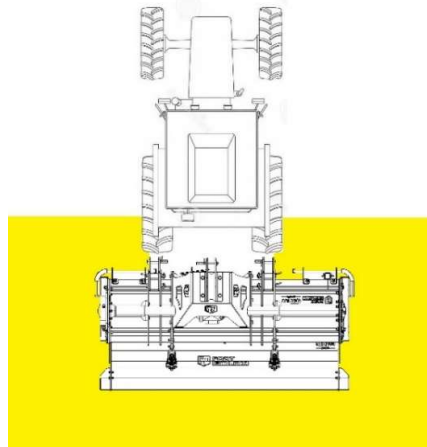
Gefahrenzone der maschine - platzhalter für bild
